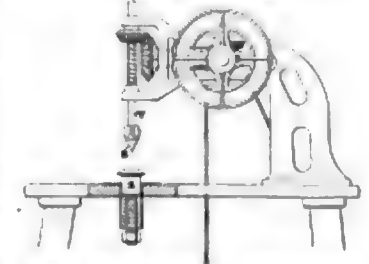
Fräsmaschine für kleine Holzarbeiten.
